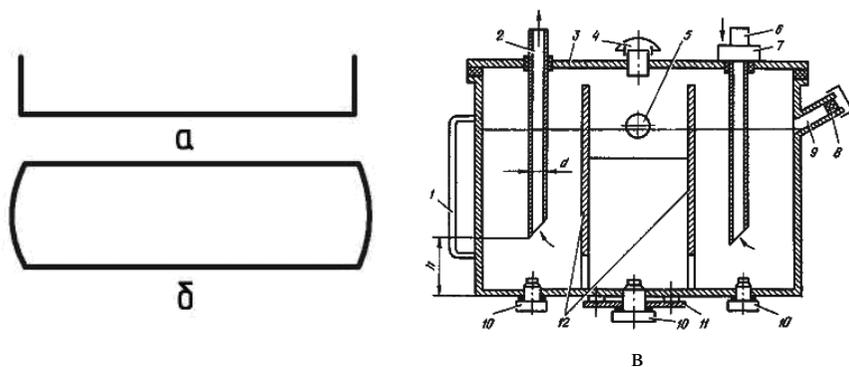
Условные обозначения баков с атмосферным давлением (а), избыточным давлением (б) и конструкция гидробака (в):
